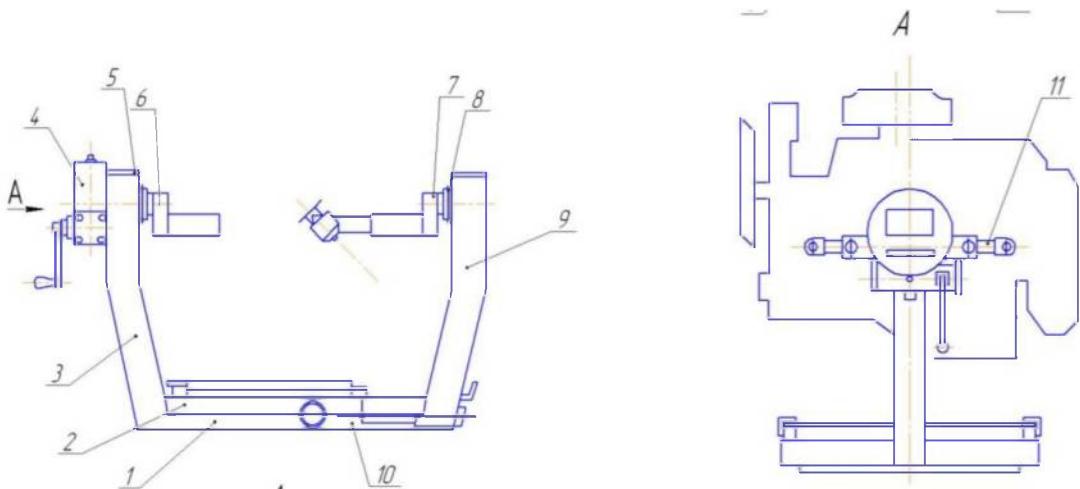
Стенд для разборки и сборки двигателей (модель С 152)
